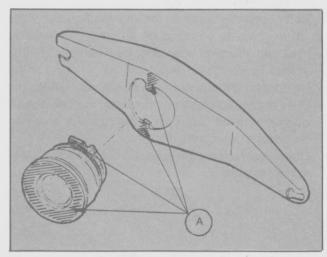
Instalación del cojinete de empuje en la horquilla de desembrague.
